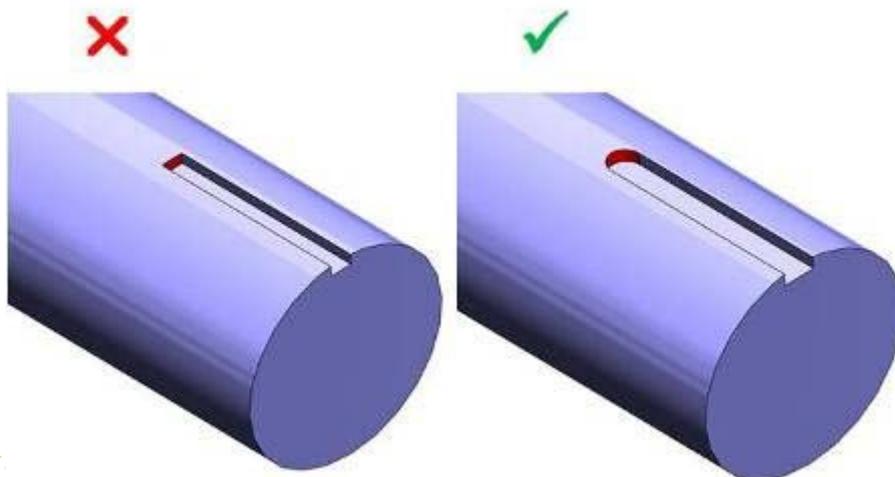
Шпоночный паз должен заканчиваться скруглением
